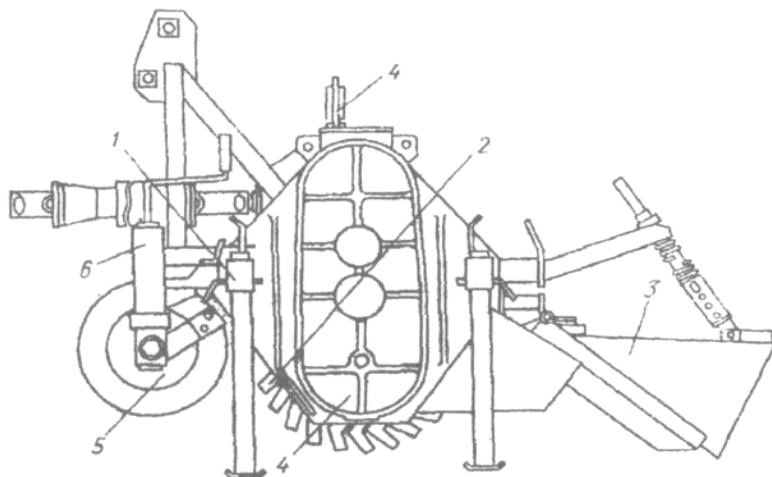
Культиватор фрезерний КФК-2,8: 1 – рама; 2 – фрезерний барабан; 3 – гребне утворювач; 4 – редуктор; 5 – опорне колесо; 6 – механізм заглиблення
